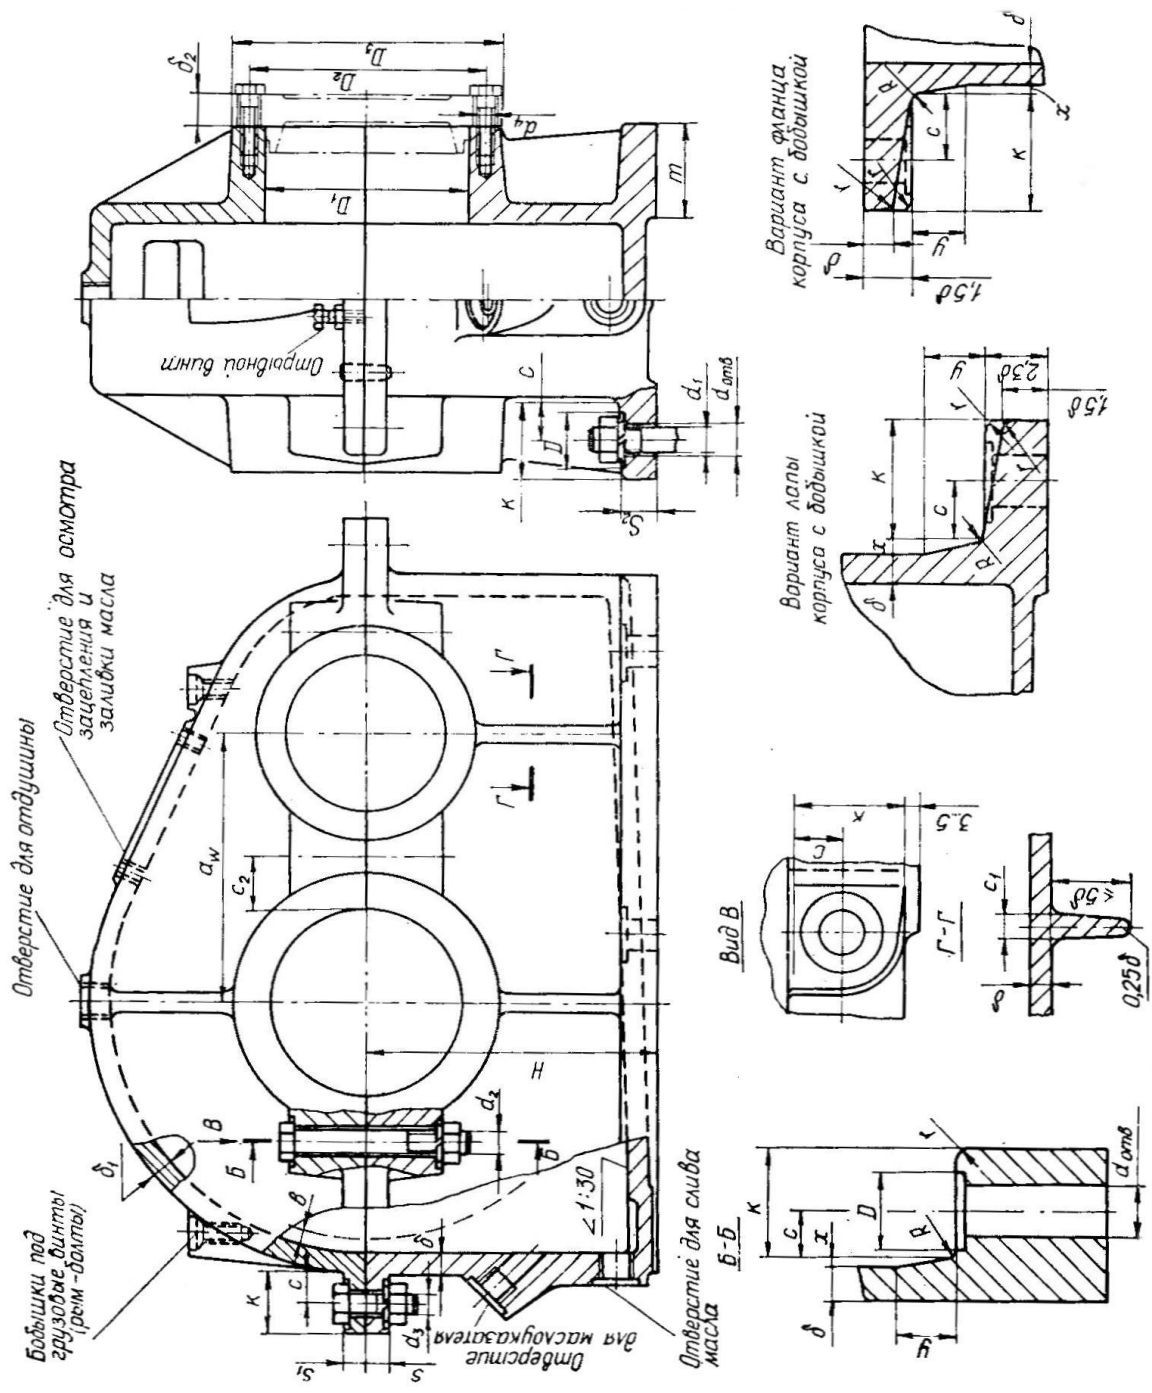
Конструктивні елементи корпусу і кришки циліндричного редуктора
